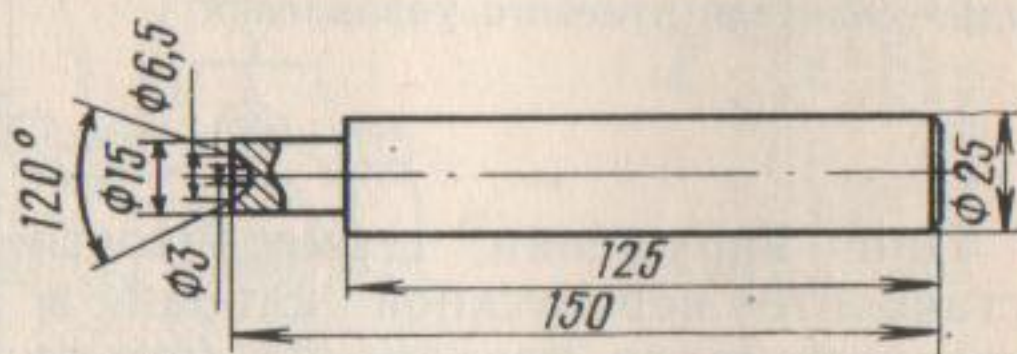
Приспособление для разборки и сборки перепускного клапана насоса гидроусилителя рулевого управления
